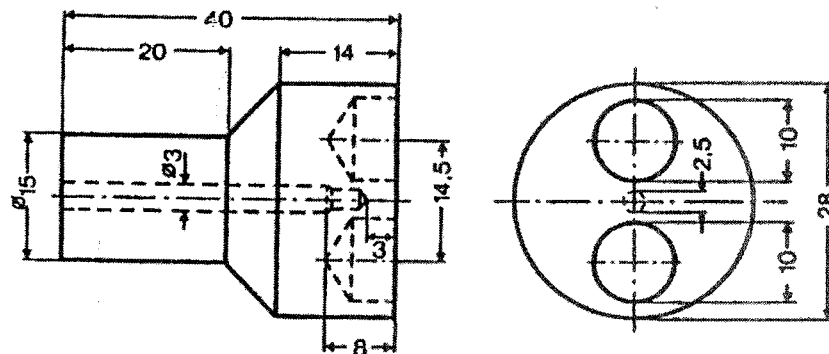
Corpo de prova de fadiga térmica destinado a simular a parte superior de um cilindro diesel. Dimensões em mm.^[4]
